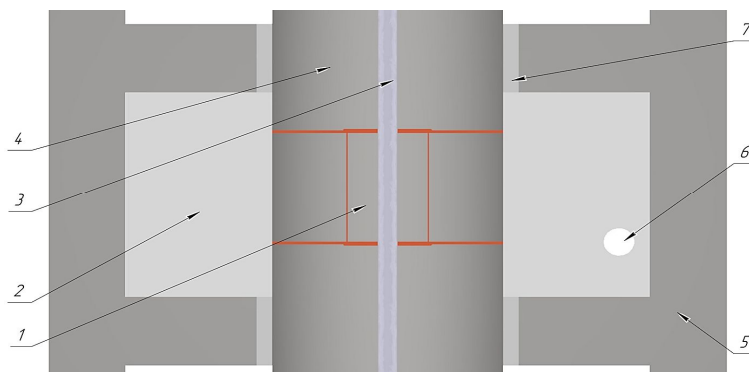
Вид сверху на образец и извлекаемую часть. 1 – извлекаемый малогабаритный образец; 2 – дно емкости для закалки; 3 – сварной шов; 4 – составной образец; 5 – рама приспособления; 6 – отверстие для слива воды; 7 – пластик.
